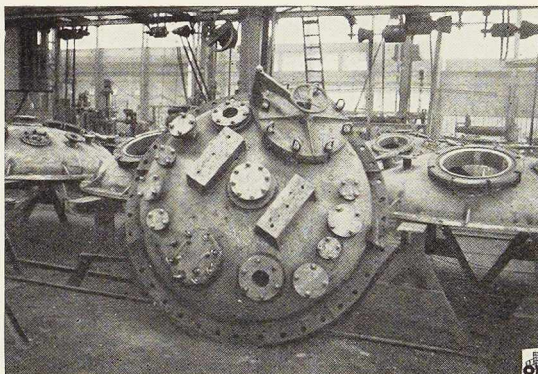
Vue d'ensemble du couvercle équipé de ses tubulures.
